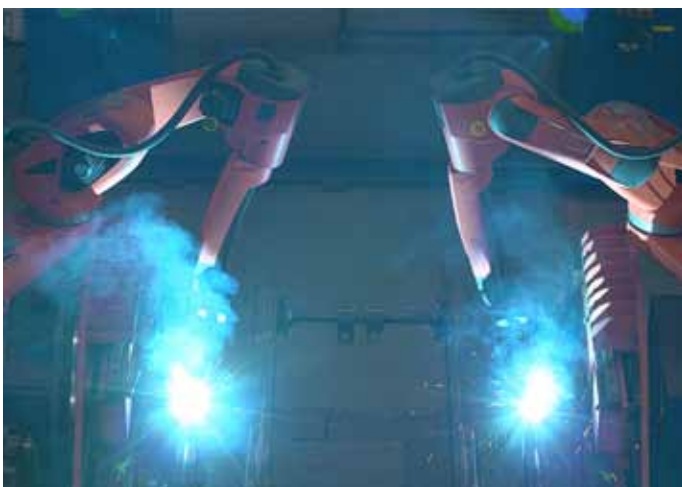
Insgesamt beschleunigen die Roboter die Schweißfertigung um mehr als 50 Prozent.
